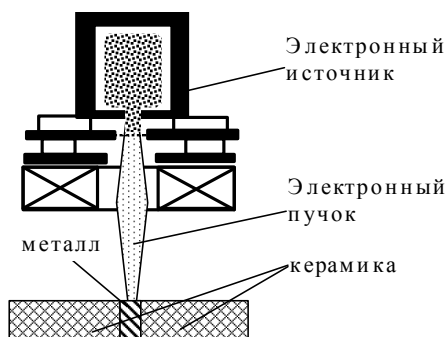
Схема установки для проведения электронно-лучевой сварки
